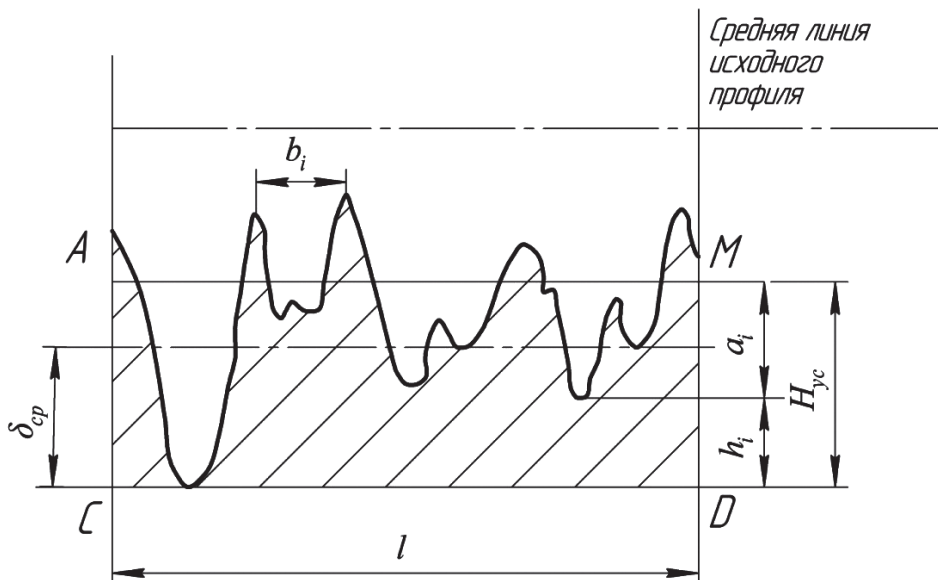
Схема образования профиля шероховатости поверхности при обработке свободными абразивами
